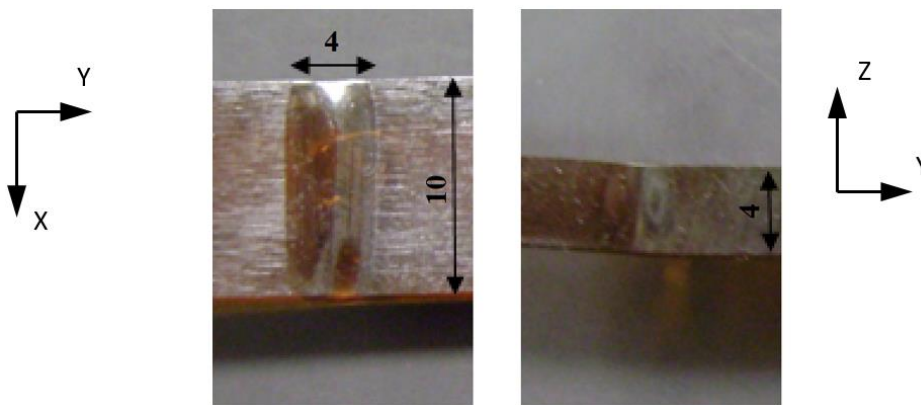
Echantillon d'interaction Laser - matière. À gauche : vue de dessus. À droite : vue latérale. Dimensions en mm
